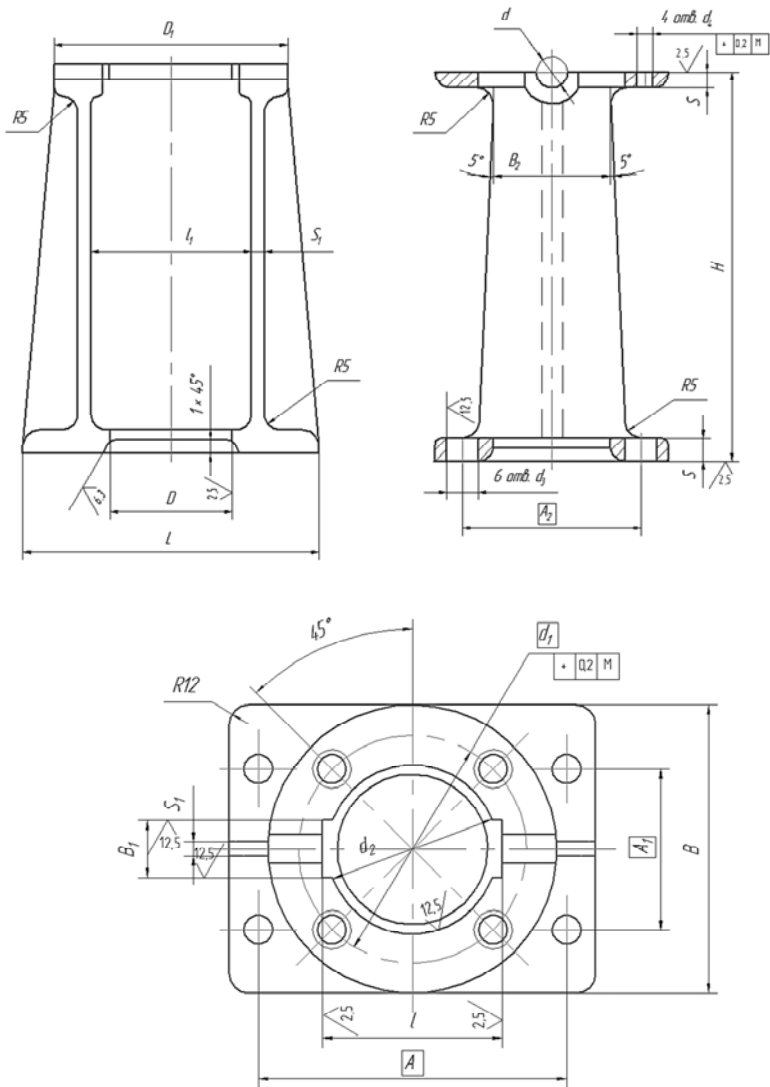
Конструкция стойки гидравлического приспособления для удаления стержней
